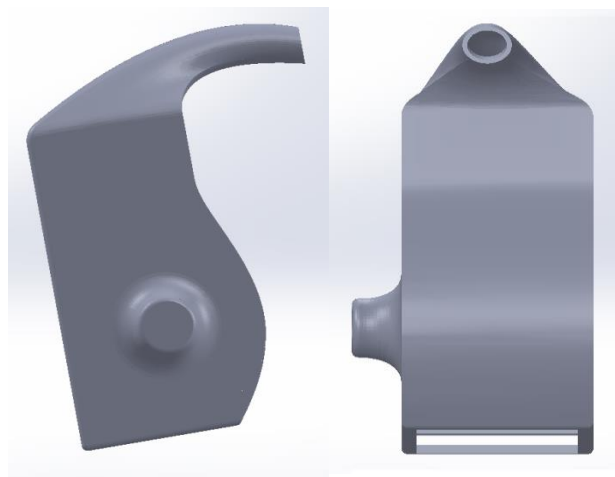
Vista lateral izquierda y vista frontal del diseño 3D del sistema termómetro-transmisor de datos.
